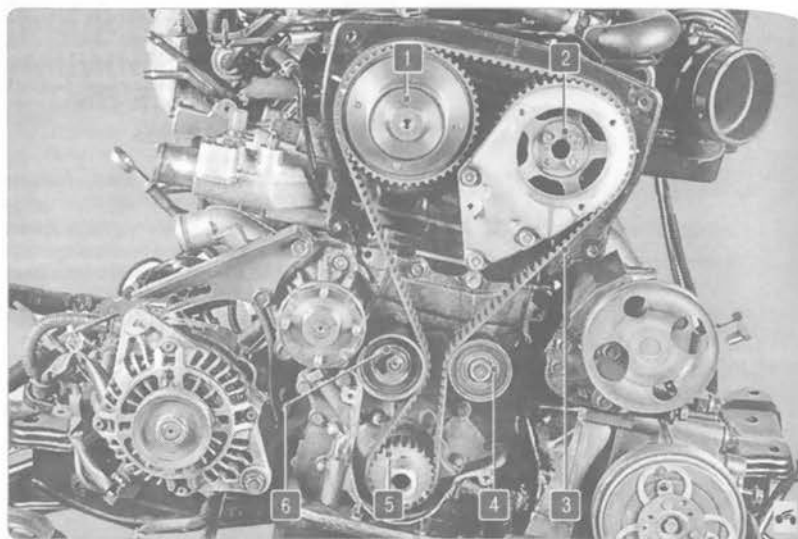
Привод газораспределительного механизма: 1 – зубчатый шкив впускного распределительного вала; 2 – зубчатый шкив выпускного распределительного вала; 3 – ремень привода газораспределительного механизма; 4 – опорный ролик; 5 – зубчатый шкив коленчатого вала; 6 – натяжной ролик
